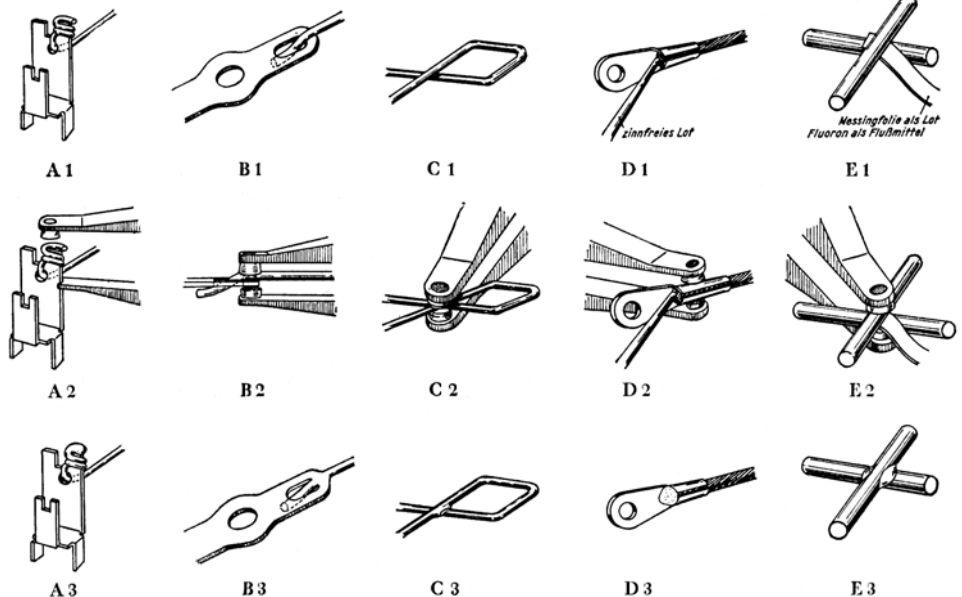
Die fünf Verbindungsarten, die mit der AEG-Kleinschweißzange möglich sind. A = Kopfschweißen an verzinnter Eisenöse und Kupferdraht, B = Schmelzschweißen an Messingöse und Kupferdraht, C = Widerstandsschweißen an Eisendraht, D = Weichlöten an Messingkabelschuh und Kupferlitze, E = Hartlöten an Kupferdraht. 1 bezeichnet stets die zum Schweißen bzw. Löten vorbereiteten Verbindungen, 2 den Ansatz der Zange, 3 die fertig geschweißten bzw. gelöteten Verbindungen.
